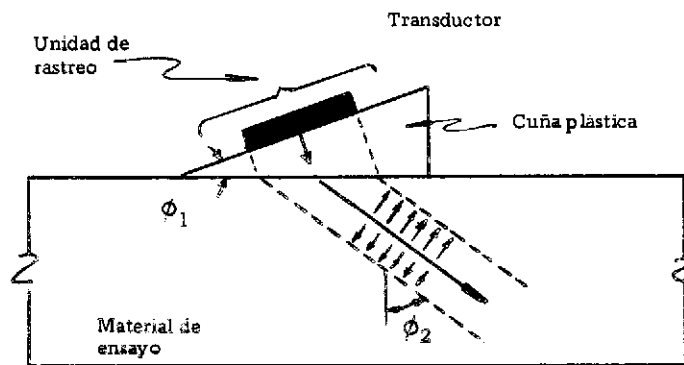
Cuña plástica que por conversión y refracción de las ondas longitudinales genera ondas transversales.
